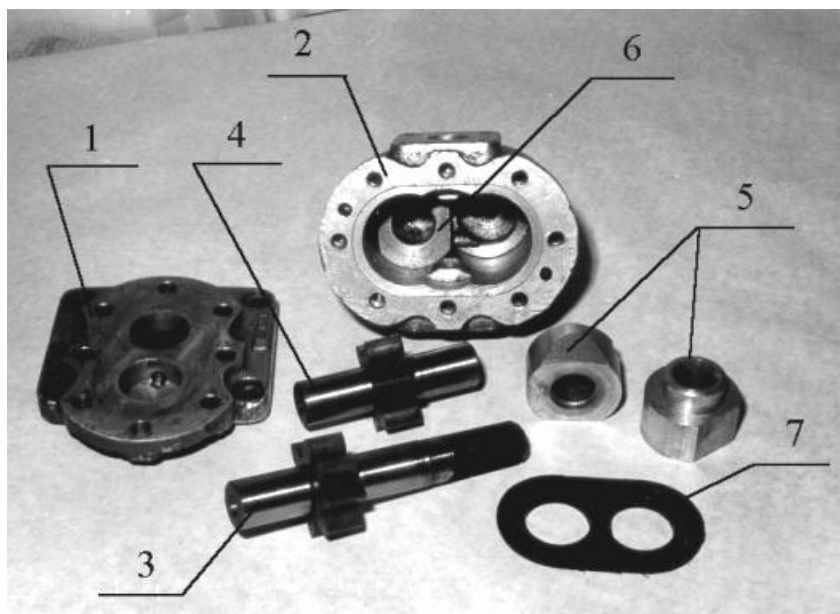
Основні деталі насоса типу НШ-У2 1 - кришка: 2 - корпус: 3 - ведуча шестірня; 4 - ведена шестірня; 5 - верхні рухомі втулки: 6 - нижні втулки; 7 - гумовий ущільнювач.
